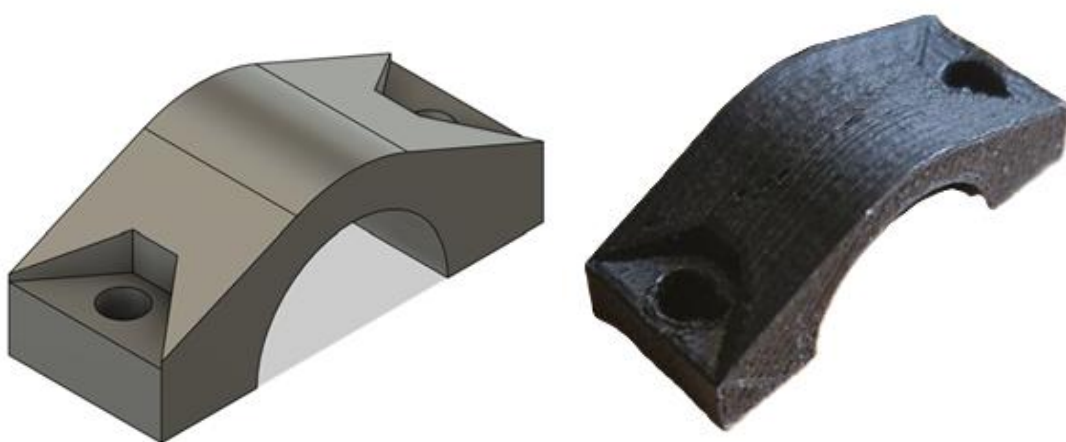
Кришка корпусу кріплення лінійних підшипників
